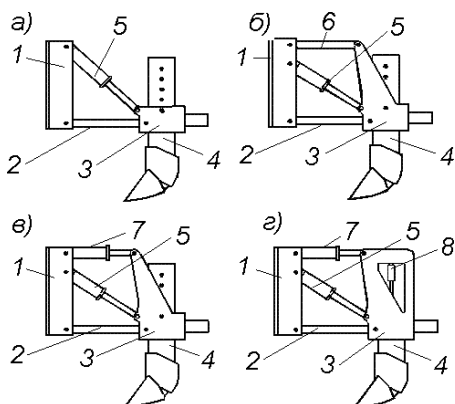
Типы рыхлительного оборудования: а) – трёхзвенное; б), в), г) – четырёхзвенное; 1 – опорная рама; 2 – нижняя тяговая рама; 3 – рабочая балка; 4 – рыхлящий зуб; 5 – гидроцилиндры подъёма и опускания рабочей балки; 6 – верхняя тяговая рама; 7 – гидроцилиндры наклона зуба; 8 – механизм изменения вылета зуба.
